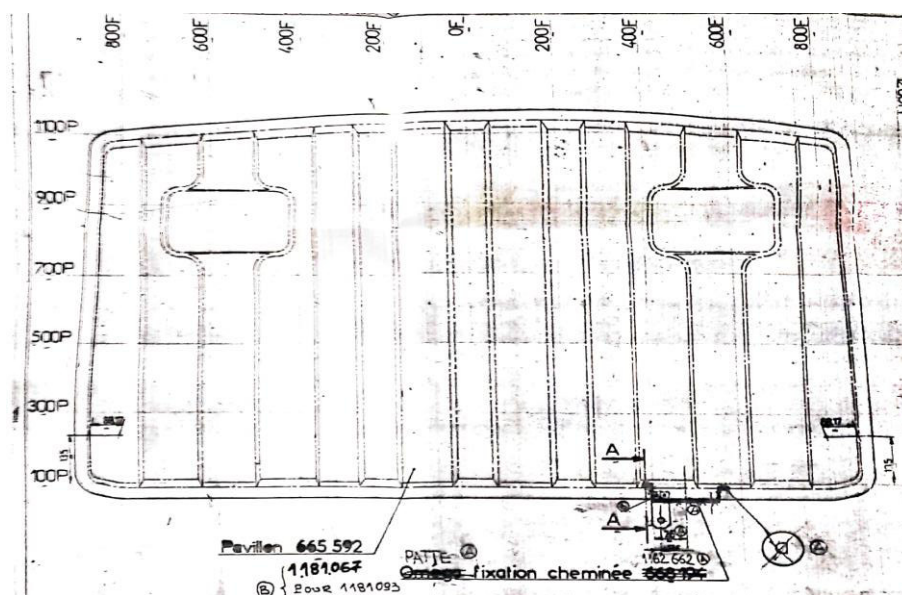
Plan de pavillon fourni par SNVI [13]
